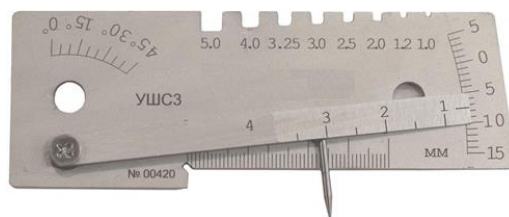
Контроль качества сварных швов напольной вешалки
